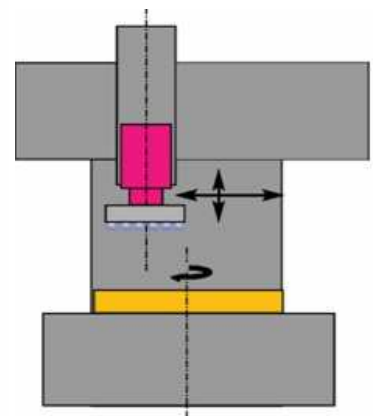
S pevným příčnickem horizontálním vřeteníkem [8]
